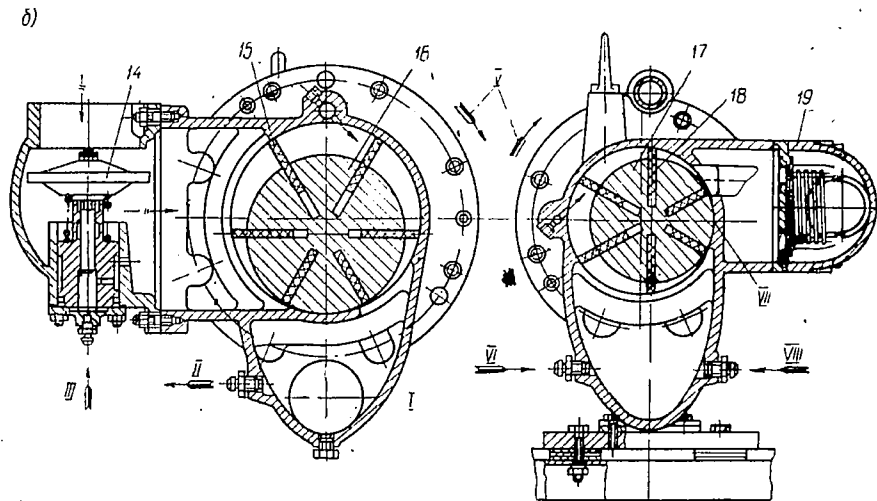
Разрезы двухцилиндрового ротационного компрессора станции ПР-10:
